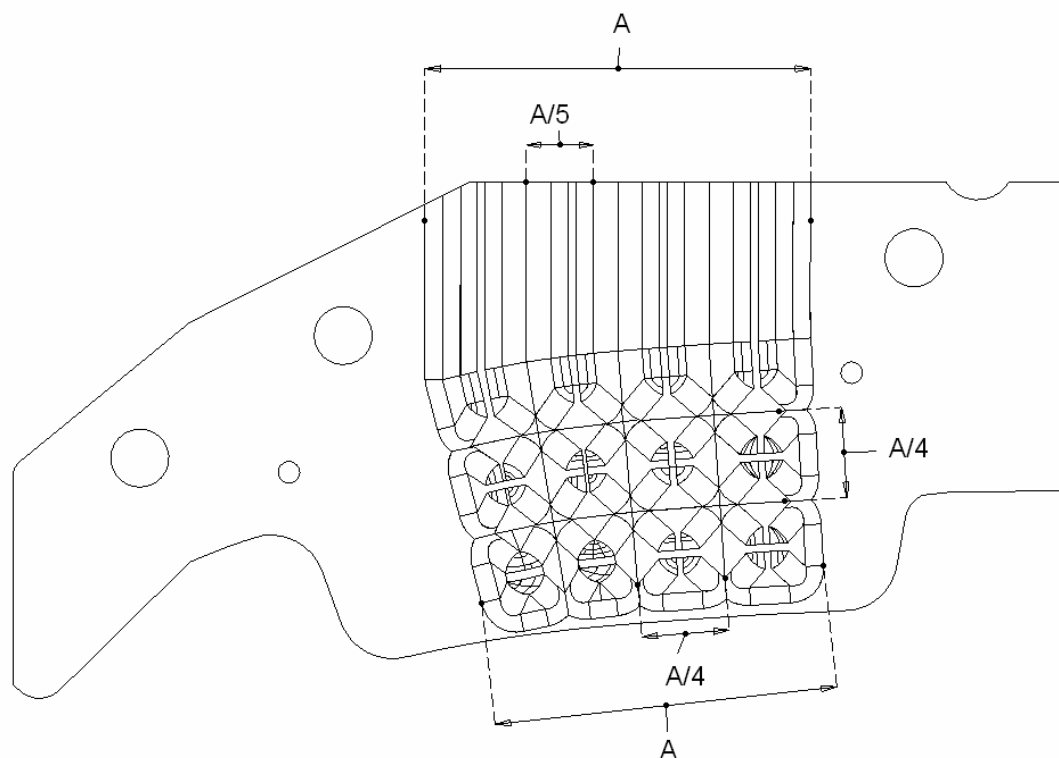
Forme de la pièce et données dimensionnelles en vue de face.
